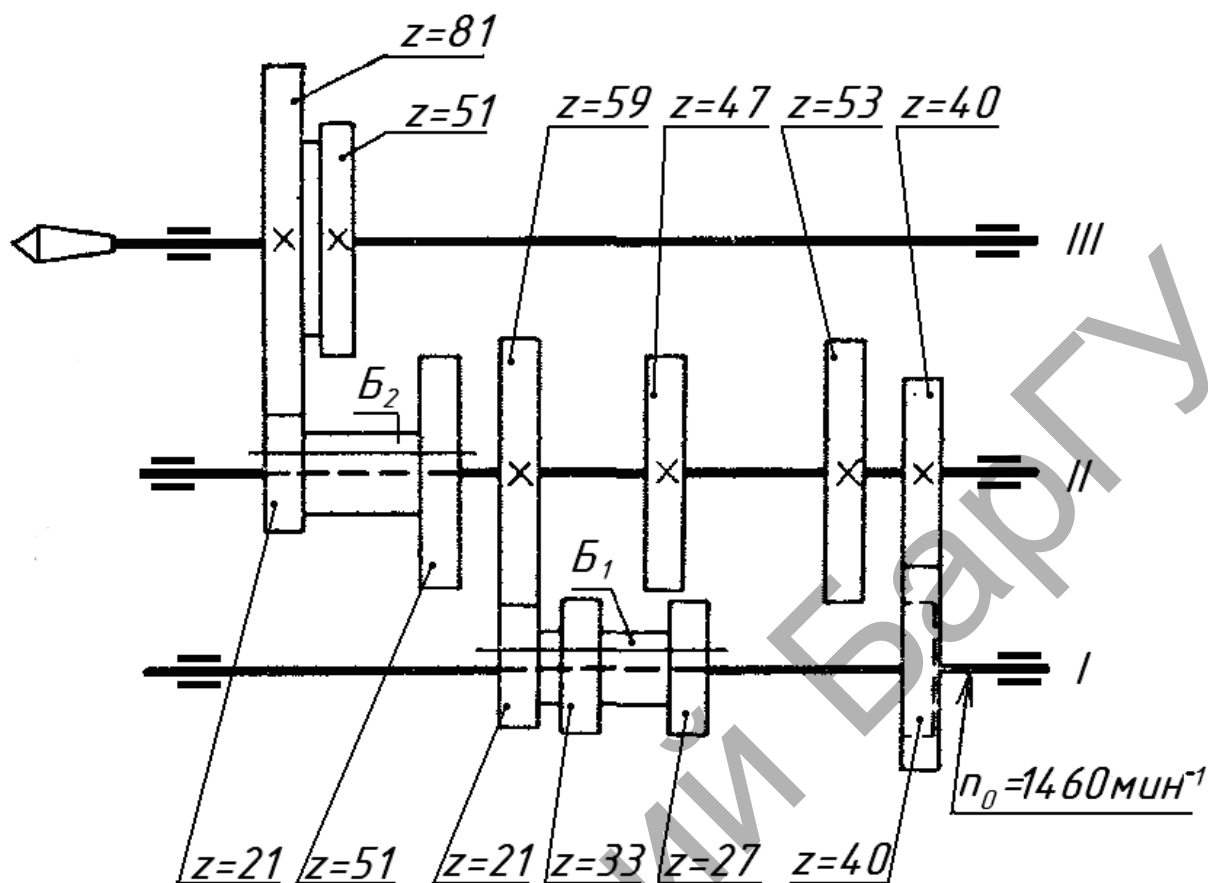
Коробка скоростей с передвижными блоками колес
